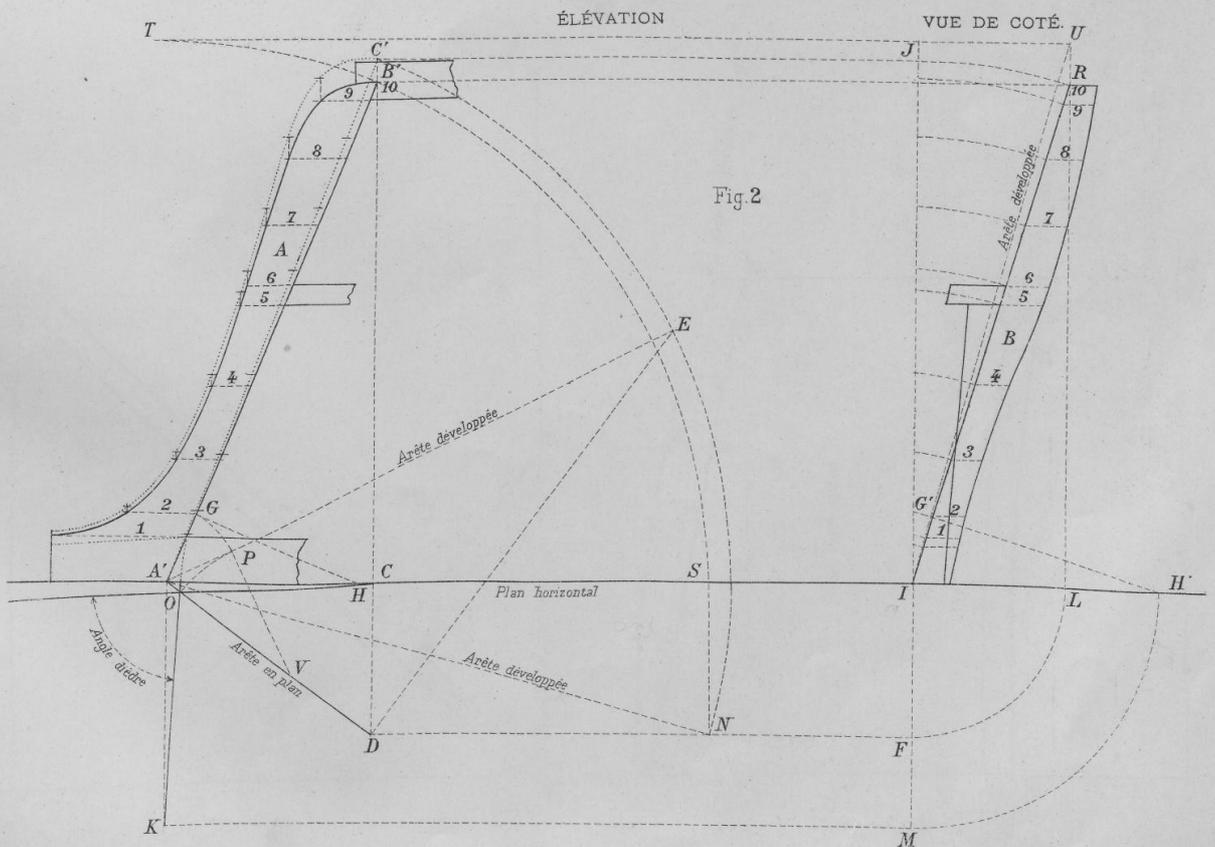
CONSTRUCTION DE L'ANGLE DIÈDRE EN PLAN HORIZONTAL ET RALLONGEMENT DU PIED DE PHAETON.
